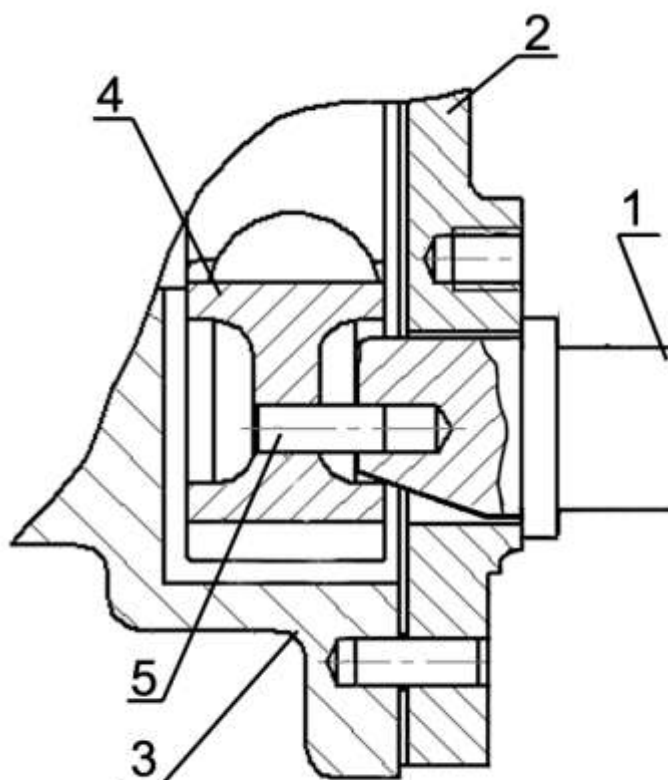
б - Установка датчика частоты вращения коленчатого вала
